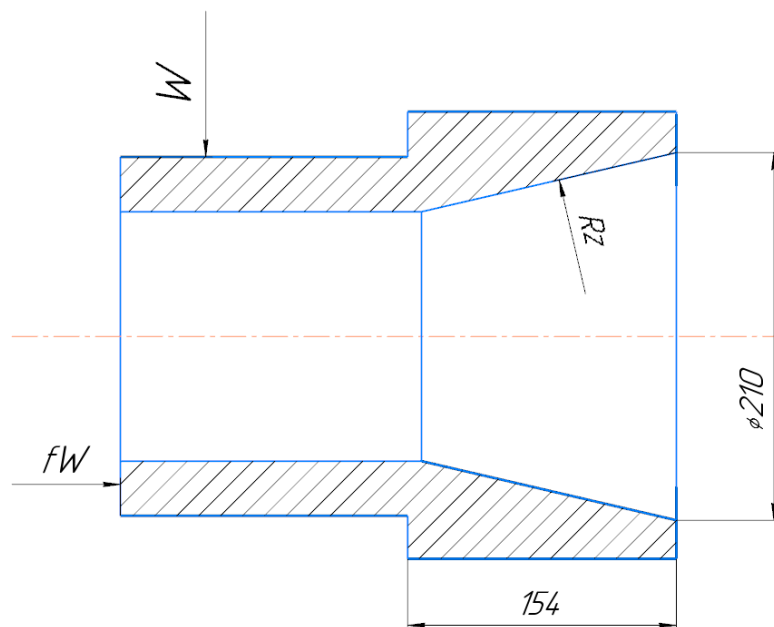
Система сил, що діють на деталь під час обробки
